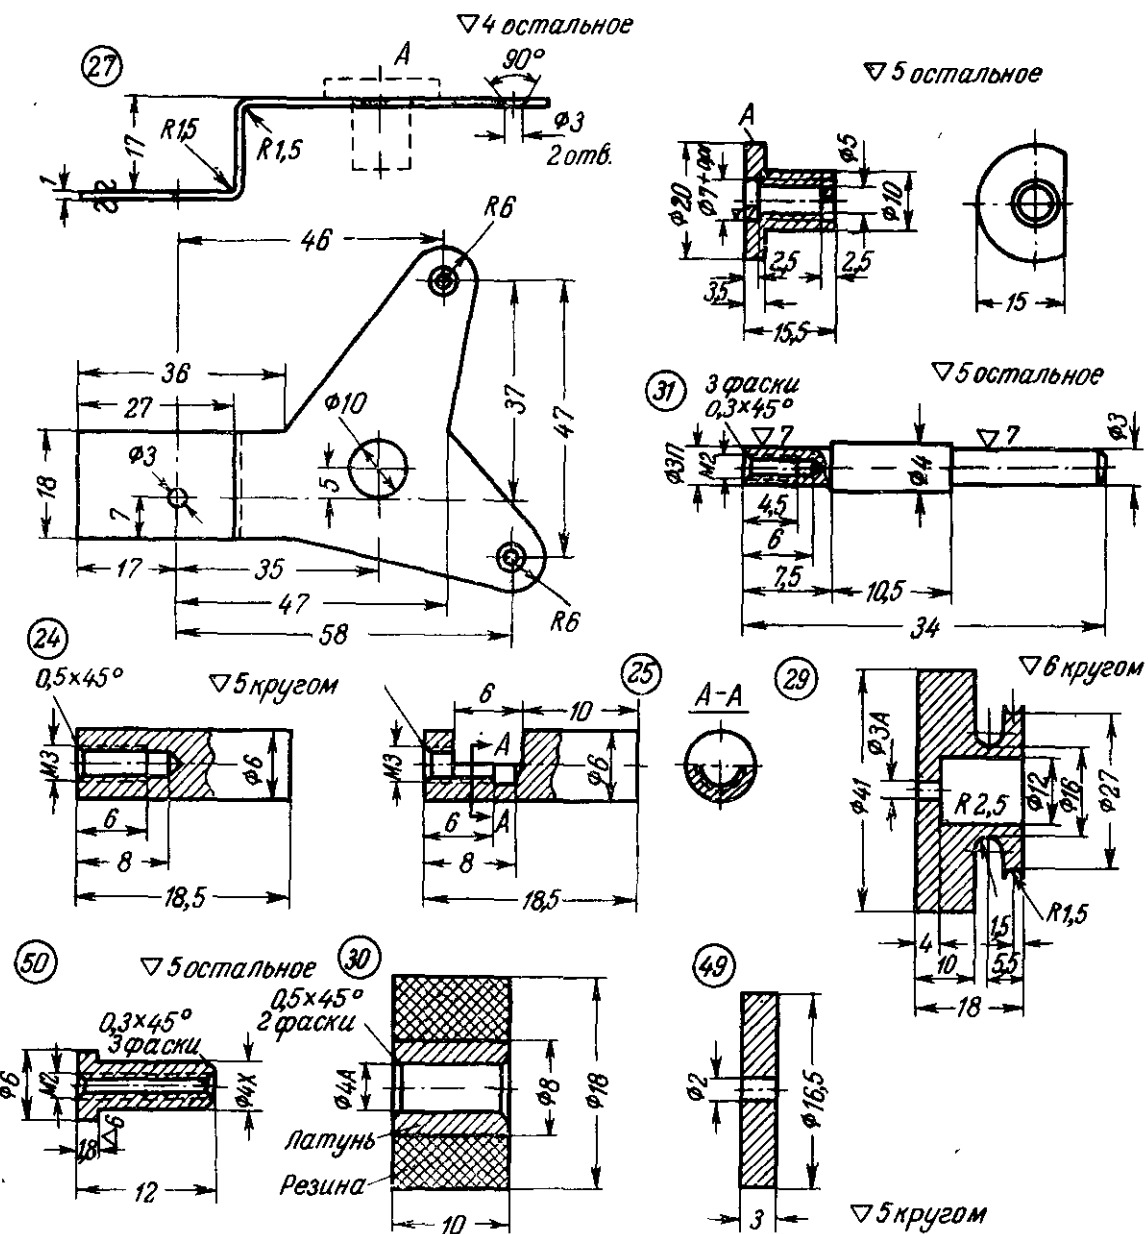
Детали узла ведущего вала (номера деталей соответствуют рис. 18).
